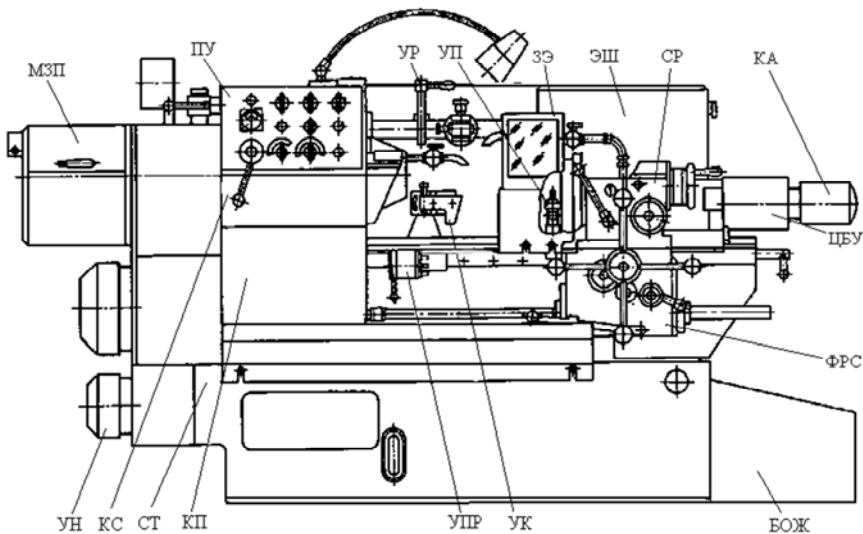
Внешний вид токарно-револьверного станка модели 1К341:
